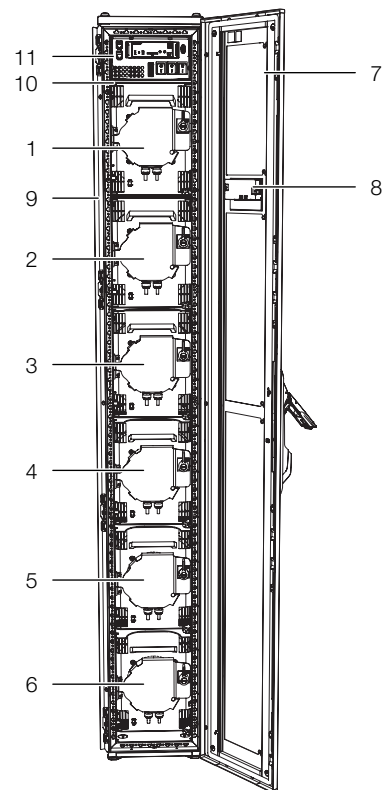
face avant Liquid Cooling Package – porte avant ouverte
